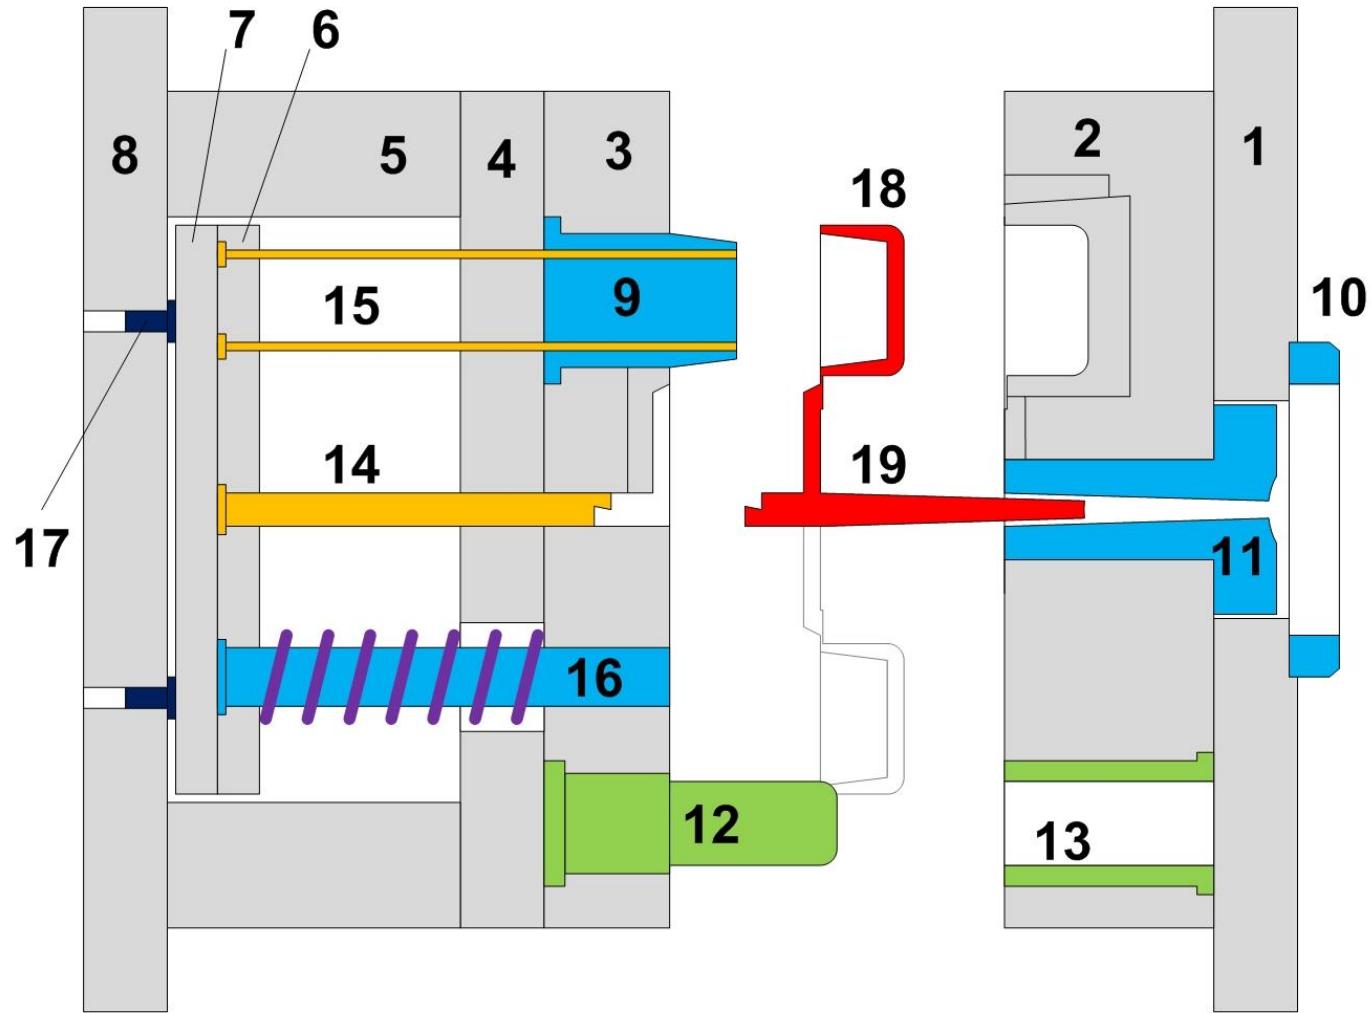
FI cu seschidere într-o treaptă (un plan de separare)
